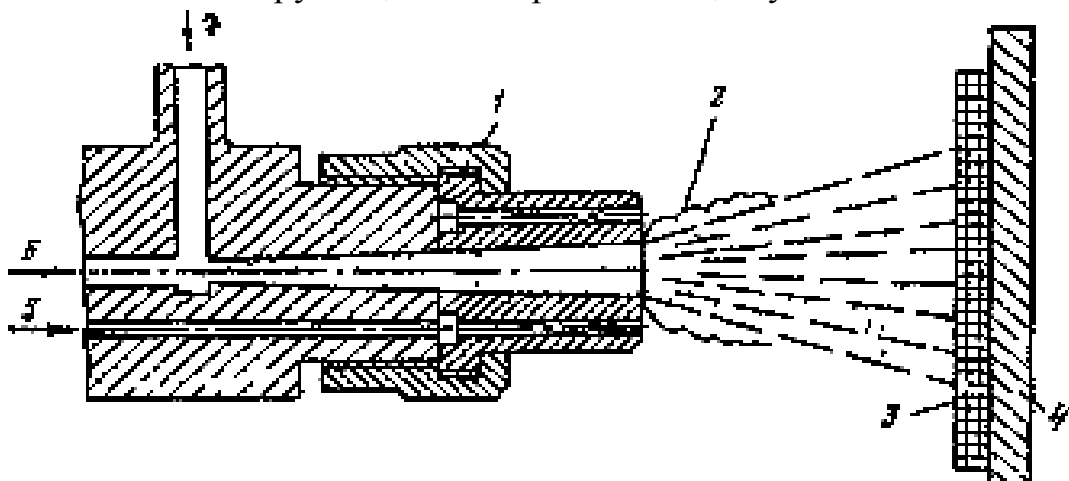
Схема розпилювальної головки газополум'яного порошкового апарату для напилення:
